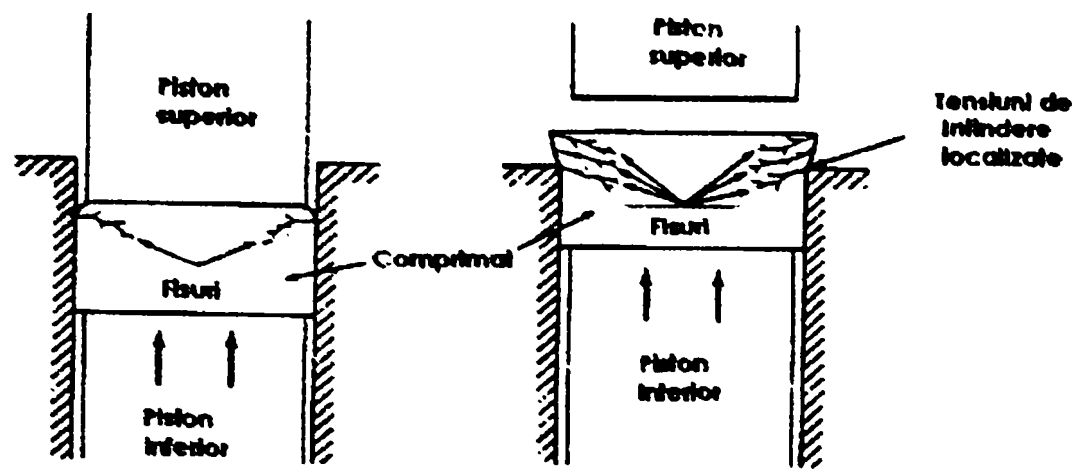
Fisurarea comprimatului la ejectare.
